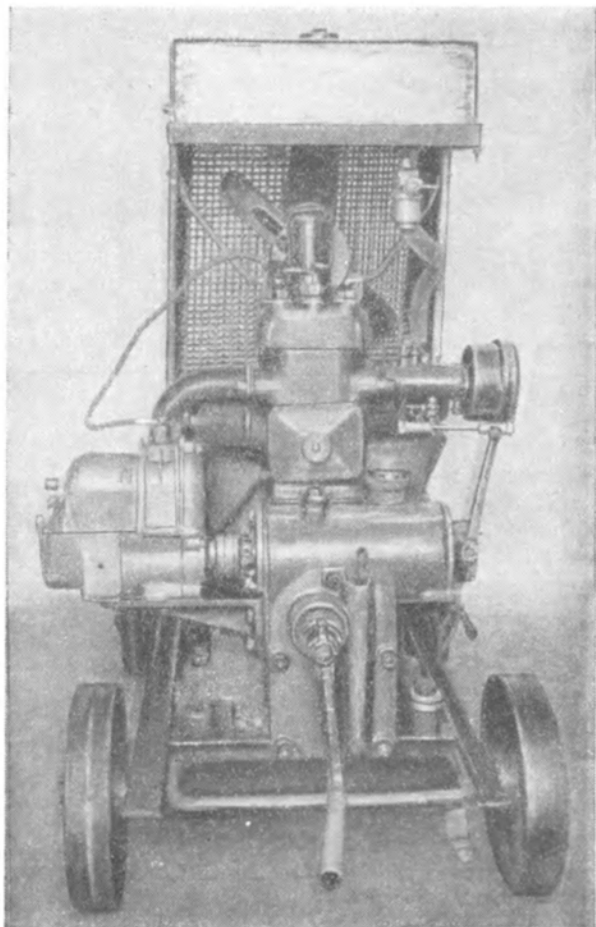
Общий вид двигателя с установленными оттяжками радиатора, новым бензокраником, новым бензопроводом, новой тягой регулятора и повернутым глушителем
